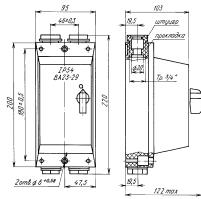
Габаритные, установочные, присоединительные размеры выключателей типа ВА23-29 одно-, двух- и трехполюсных, номинальный ток расцепителей до 25 A Степень защиты IP54. Масса не более 1,15 кг
